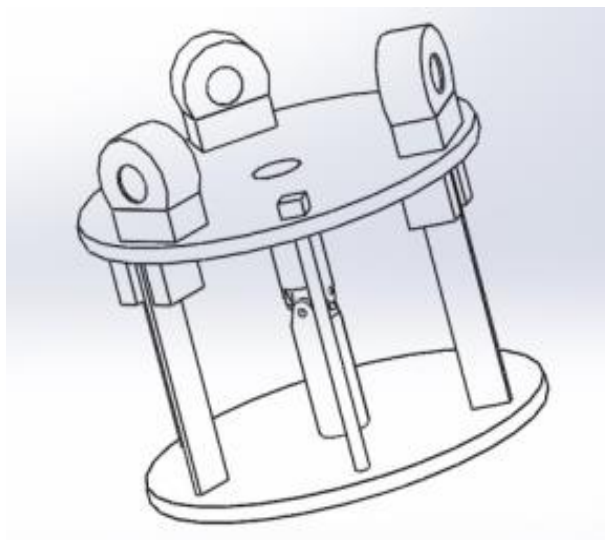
Секция сварочного робота на базе гибкого манипулятора
